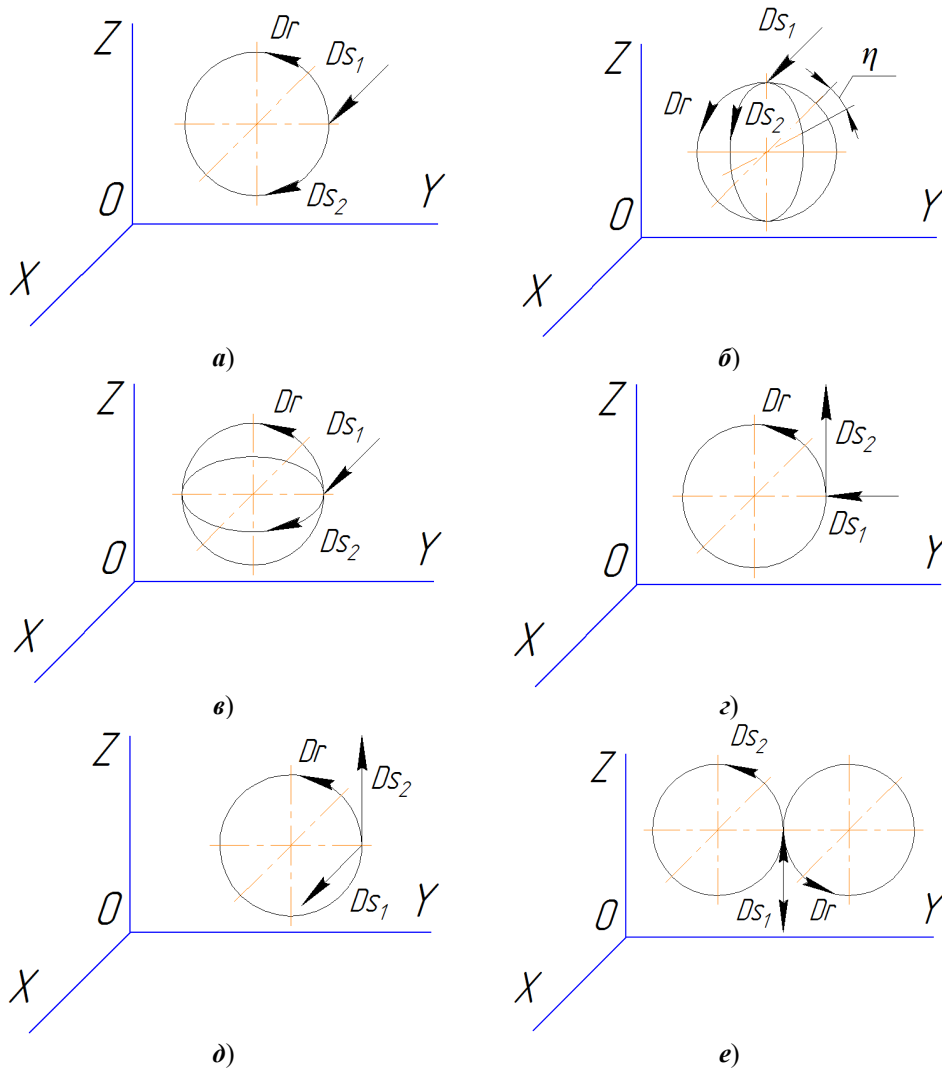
Кинематические схемы резания: а – обработка охватывающими фрезами (зенкерами) цилиндрической или конической поверхности; б, в – обработка охватывающими фрезами (зенкерами) неполной сферической поверхности; г – обработка с врезанием фрезы по дуге уступа или полузакрытой полости; д – обработка с врезанием фрезы по касательной плоской поверхности детали; е – обработка с врезанием фрезы по касательной плоской и цилиндрической поверхностями детали
